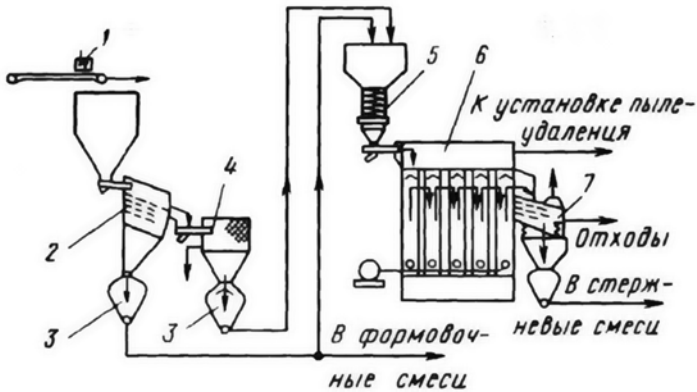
Схема пневматическом регенерационной установки: 1 — магнитный сепаратор; 2 — грохот; 3 — камерный насос; 4 — шаровая мельница; 5 — охладитель песка; 6 — многокамерный пневморегенератор; 7 — классификатор
